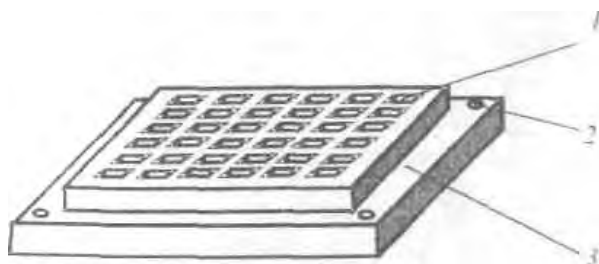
Сборочное приспособление - матрица: 1 - колодцы; 2 - отверстия для штифтов; 3 - матрица
